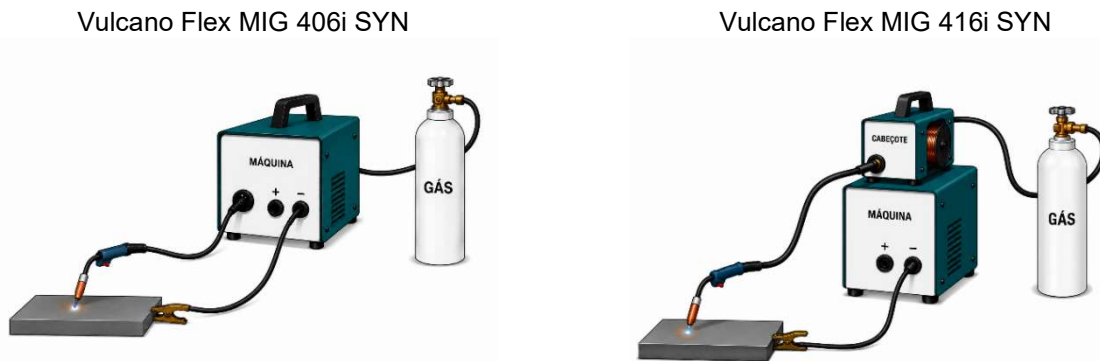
Diagrama conexão soldagem MIG/MAG.
